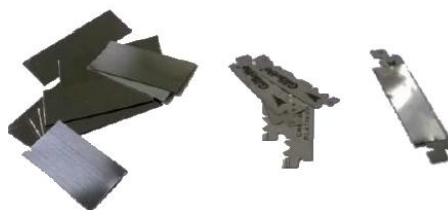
Conjunto de fitas de aço e lâminas utilizado para fabrico dos provetes DCB.
